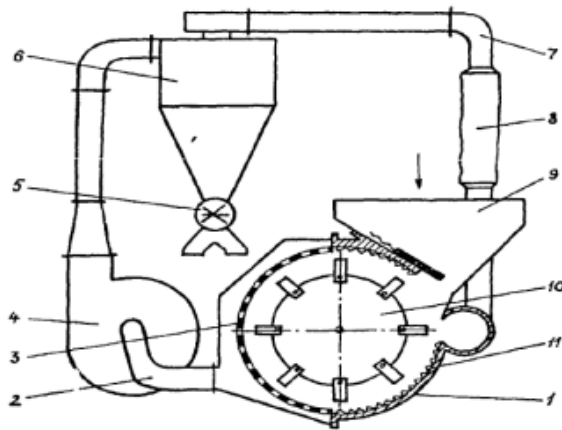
Схема кормодробарки КДМ-3,0: 1 – корпус; 2 – подвійний патрубок; 3 – решета; 4 – вентилятор; 5 – шлюзовий затвор; 6 – циклону; 7 – трубопровід; 8 – фільтр; 9 – бункер; 10 – дробильний барабан; 11 – деки.
